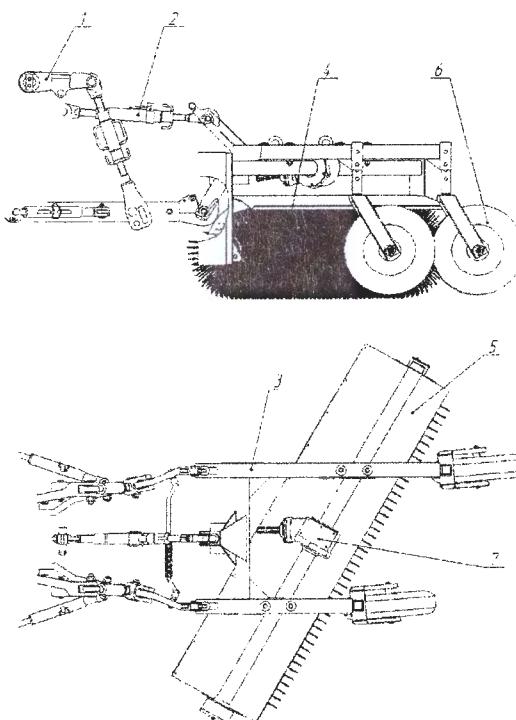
Щеточное оборудование 1 - гидроподъемник; 2 - тяга верхняя; 3 - рама; 4 – вал с ворсом; 5 - кожух щетки; 6 - колесо опорное; 7 – навеска щетки.
